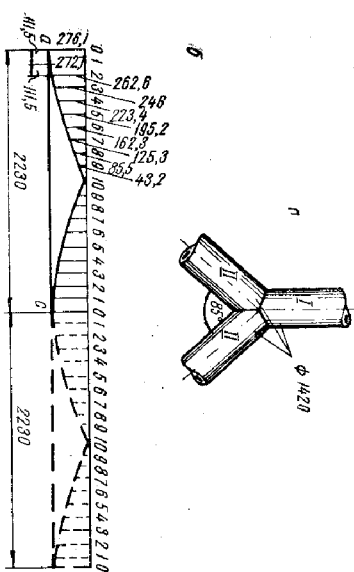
Сварной тройник разветвленного (штамп).
